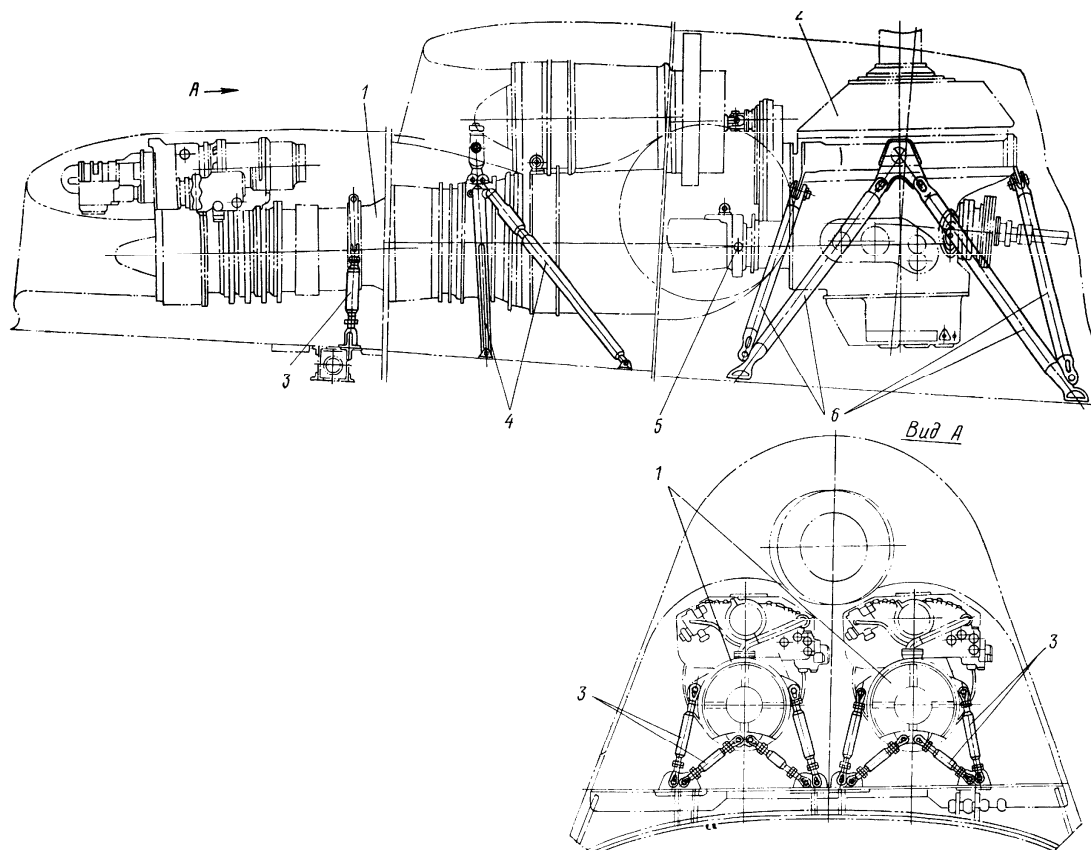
Схема крепления двигателей и редуктора на вертолете:
